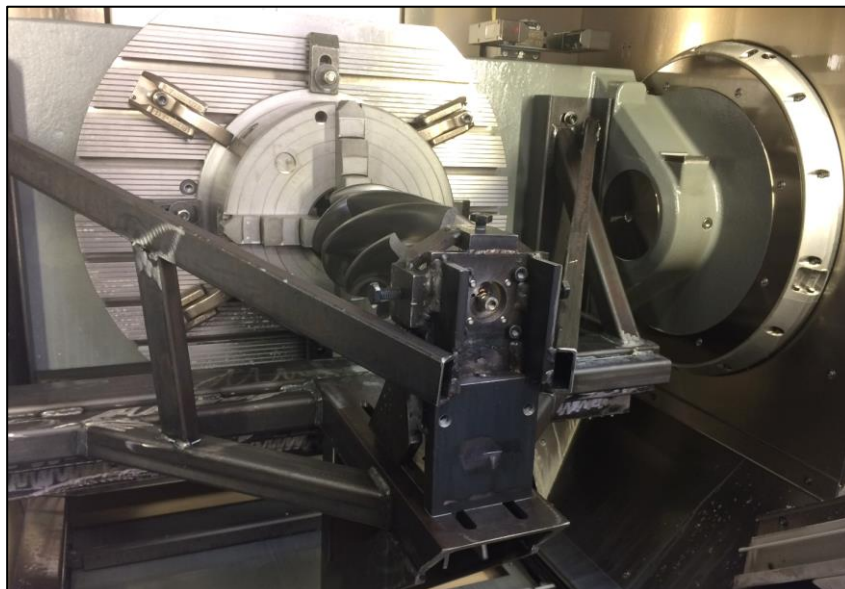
Dual-Lead-Nebenrotor auf Fünffachsfräse mit geschweißter Vorrichtung zur Verringerung der Durchbiegung.
